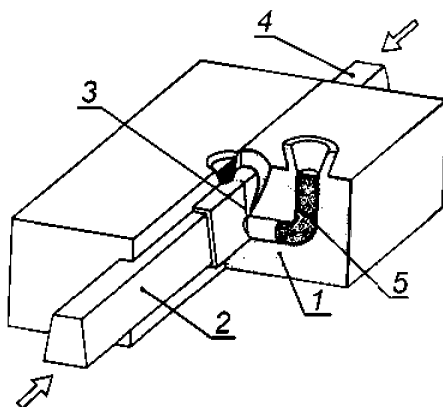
Сварка шляпкой гвоздя
